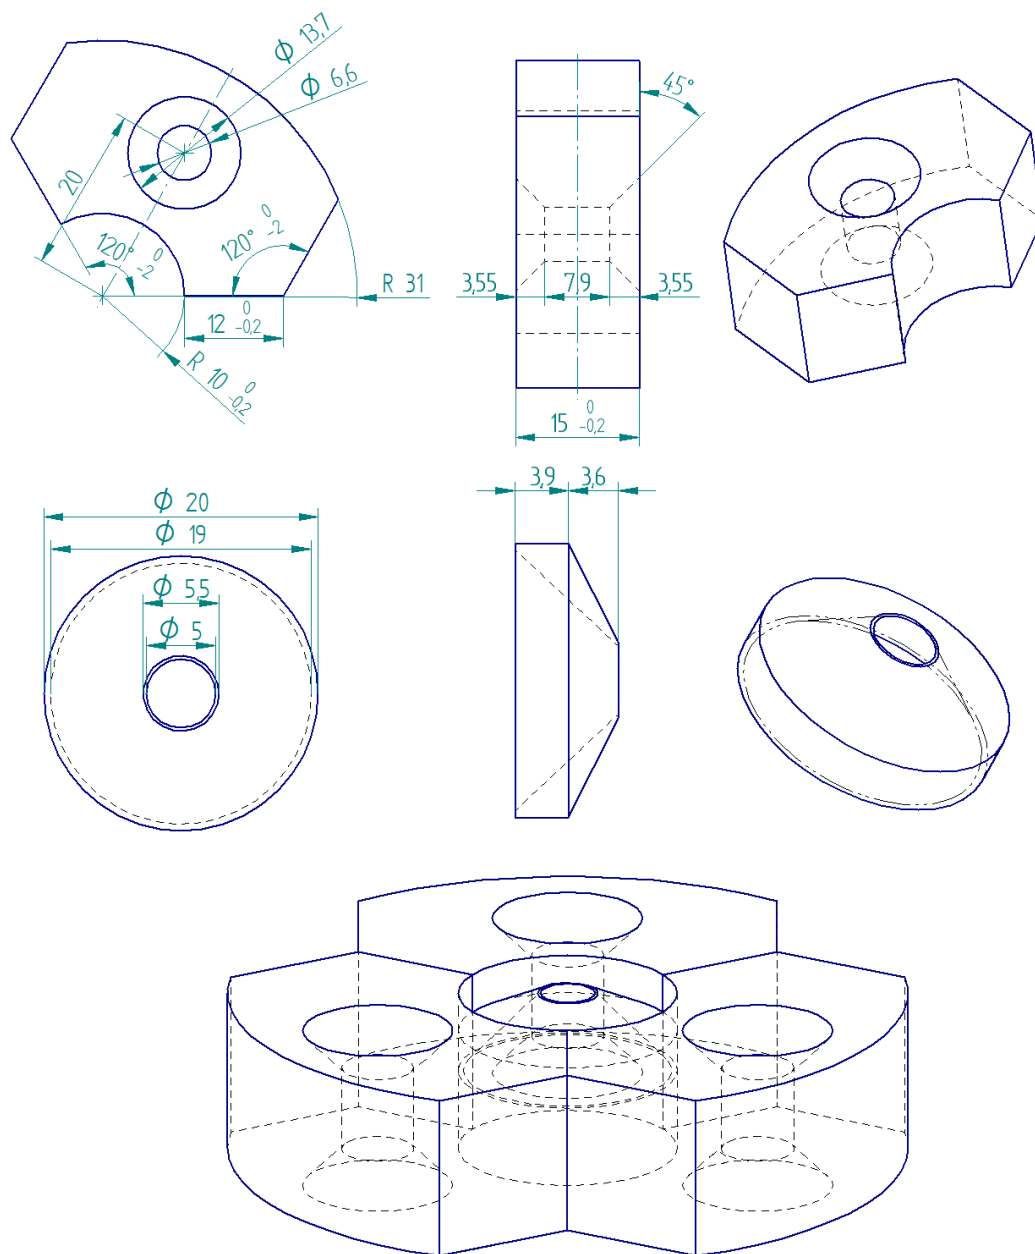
CAD Zeichnungen eines einzelnen Magnets, der Polkappe sowie des zusammengesetzten Dreiermagneten
